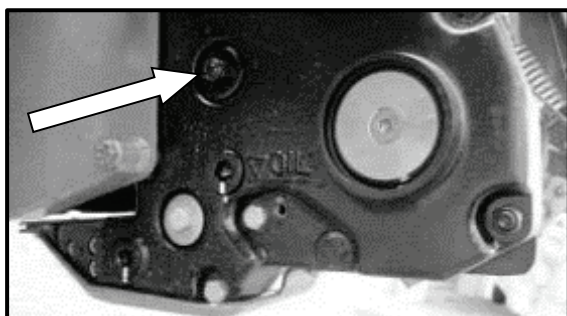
[2] Engranaje de entrada y barra de corte (2)
